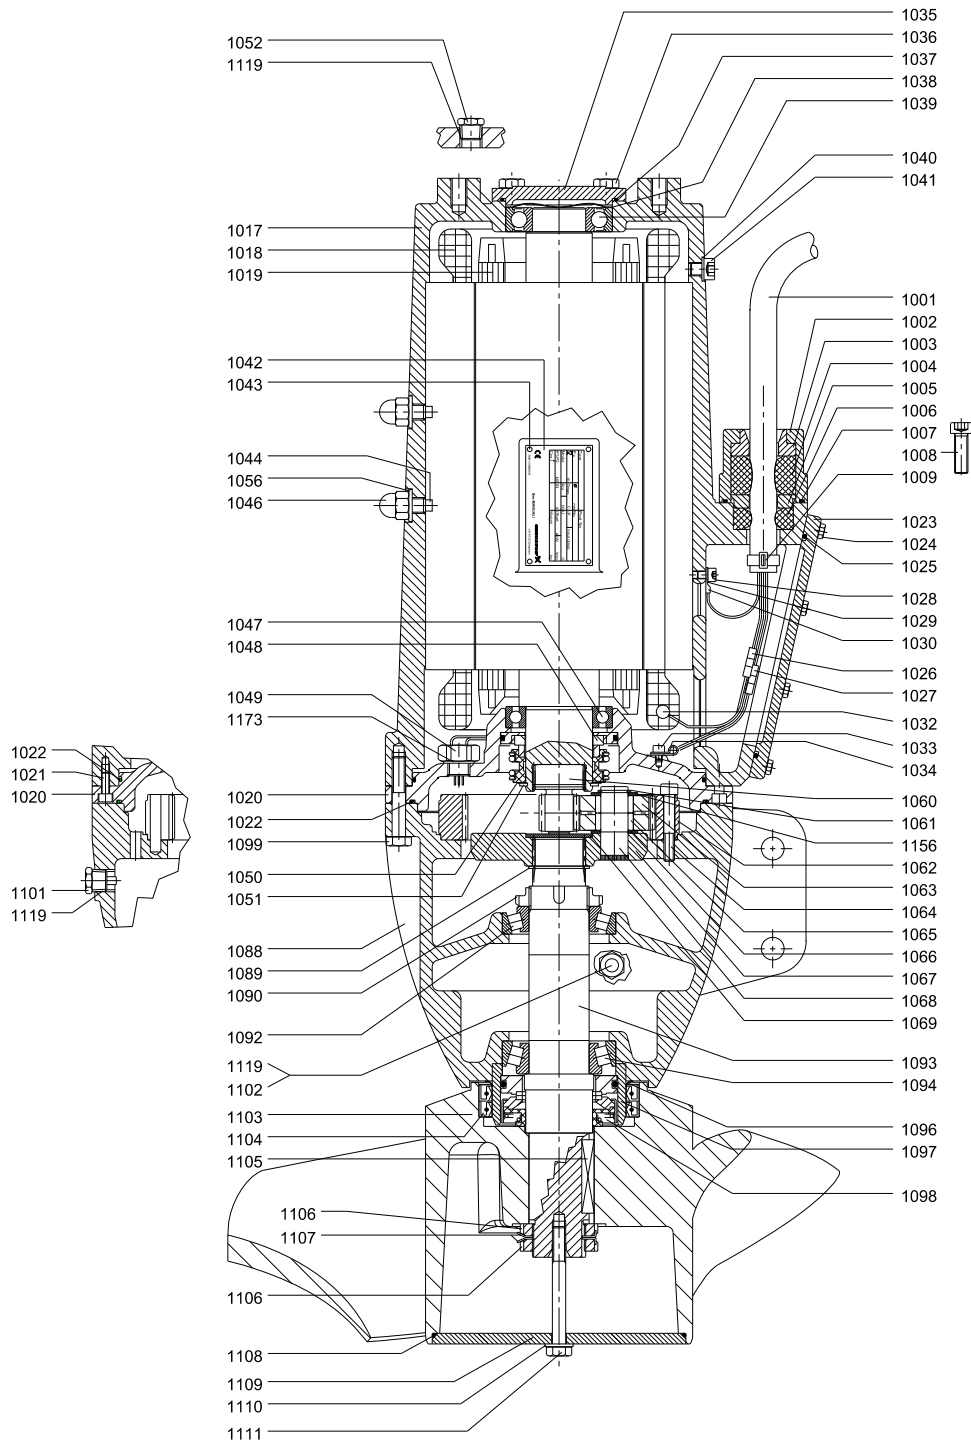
Чертёж в разрезе, SRP.65.50.xxx, SRP.80.50.xxx и SRP.100.50.xxx
